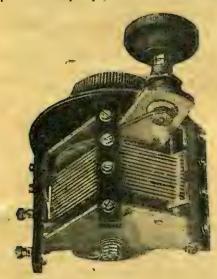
Конструкция фабричного конденсатора с ременной передачей.
